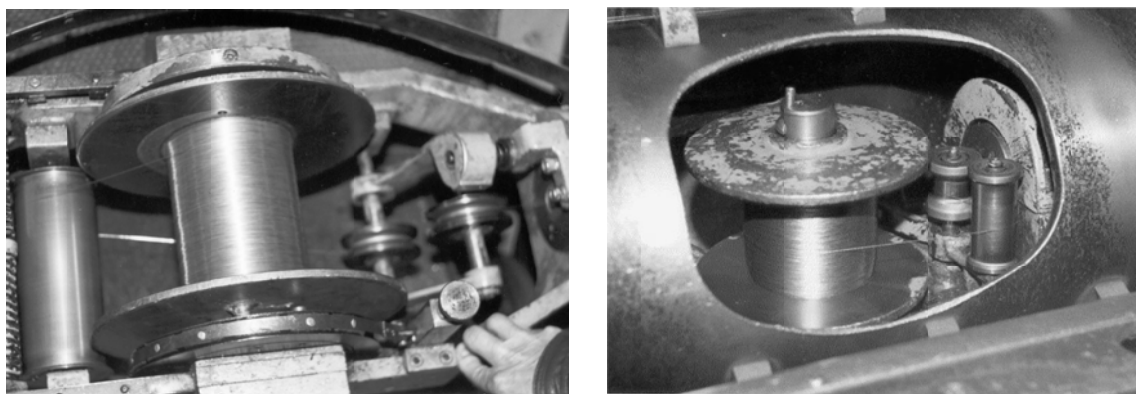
Внешний вид каретки канатовьющей машины с горизонтальным и вертикальным расположением питающей катушки
